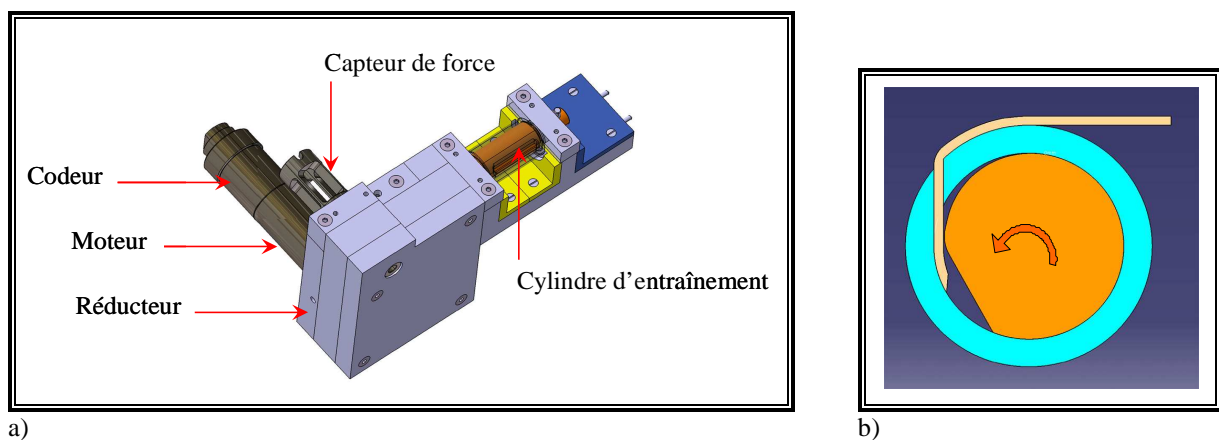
a) Représentation schématique d'un module de la machine et b) vue de côté d'un verrou.
